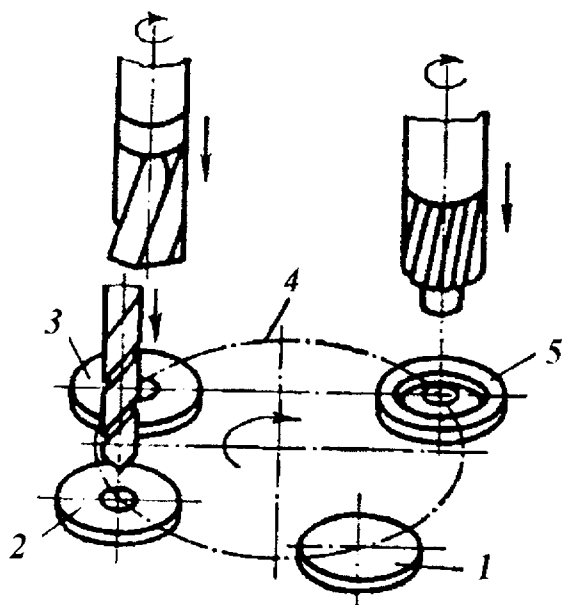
Четырехпозиционная обработка детали на трехшпиндельном станке: 1 – установка и съем детали; 2 – сверление; 3 – зенкерование; 4 – стол; 5 – зенкование
